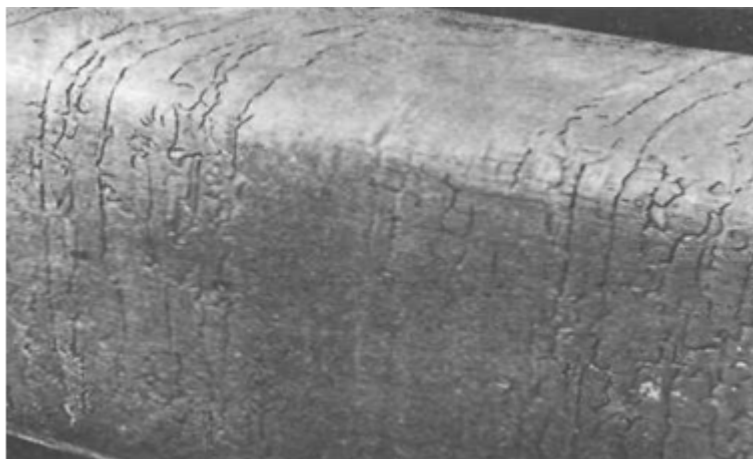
Внешний вид слитка стали 12X18H10T с заворотами корки на поверхности
